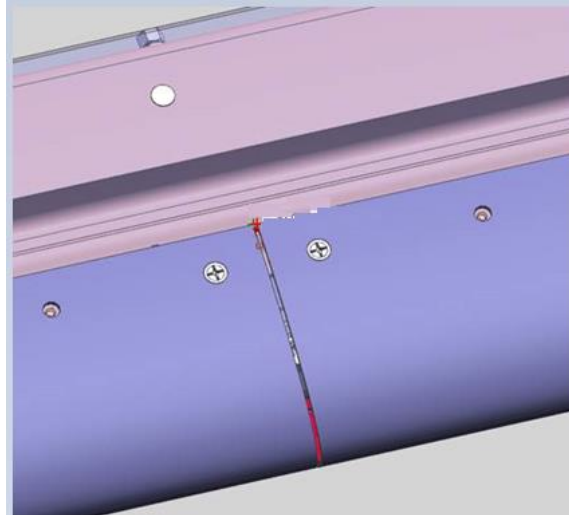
Dış-İç Duvar Montaj Fikstürü
